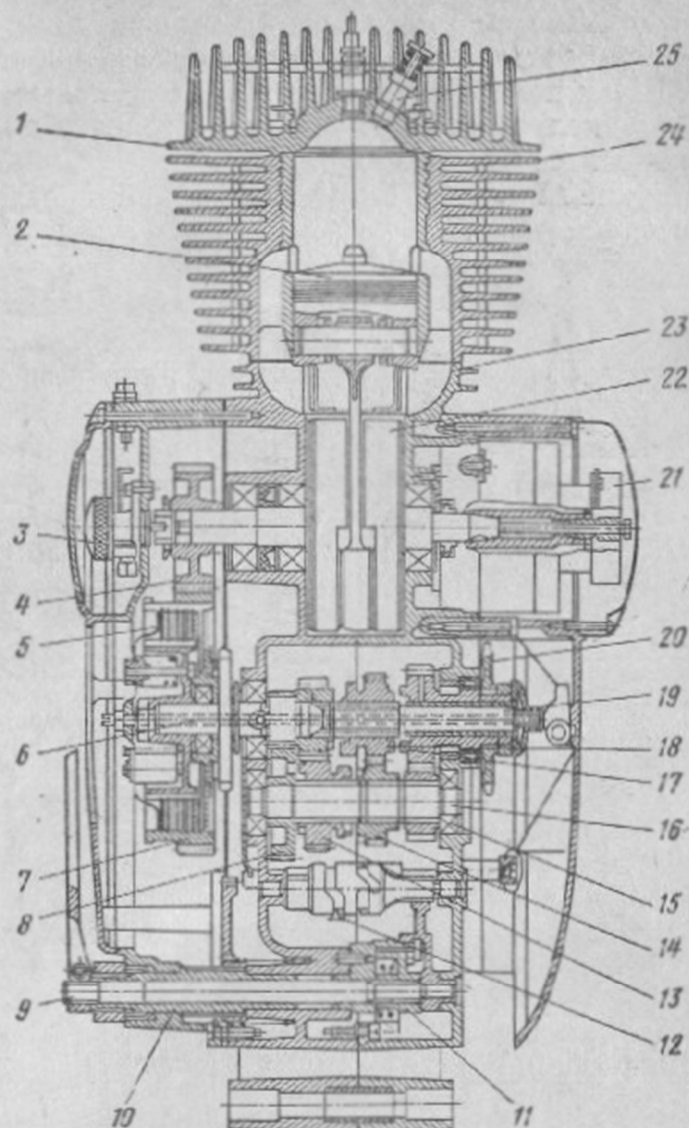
Силовой агрегат «Иж-Планета-Спорт» в разрезе:
